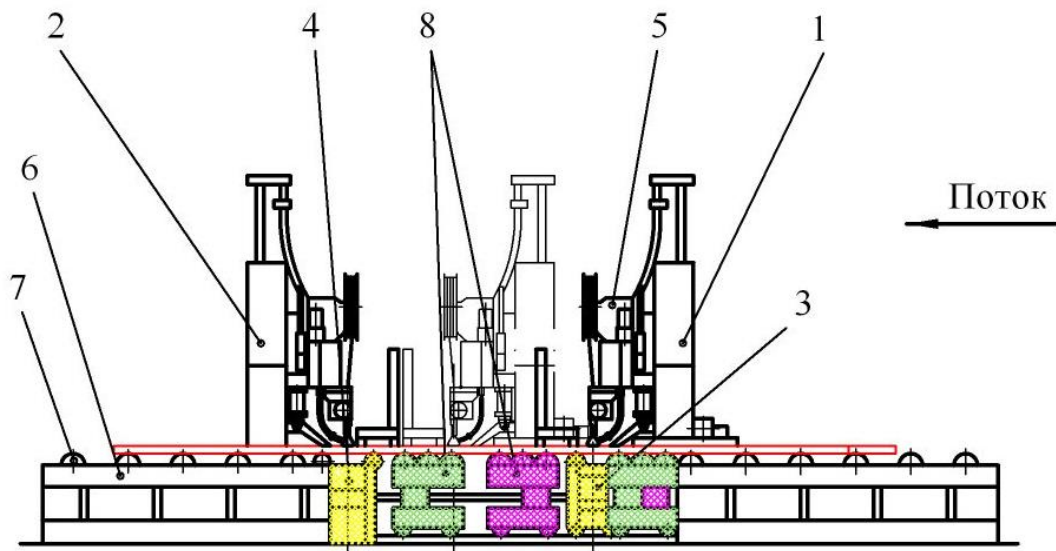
Универсальный односторонний стенд автоматической сварки первой стороны листовых полотнищ:
